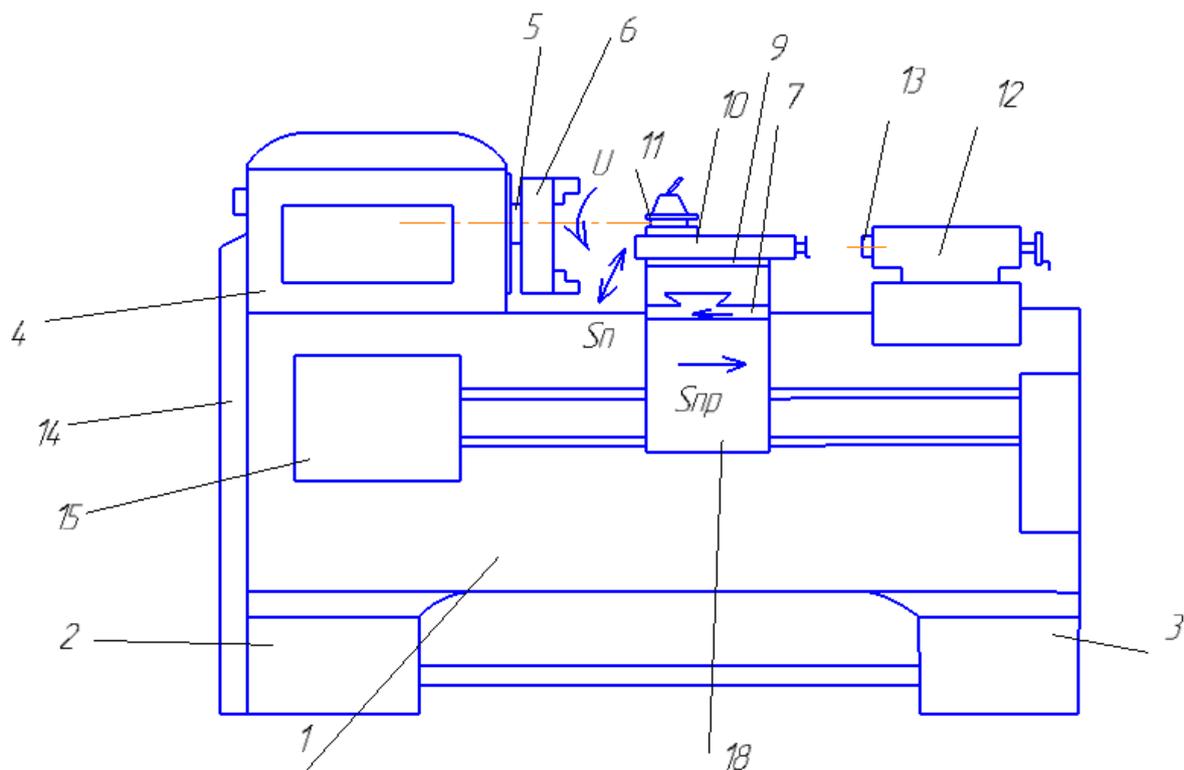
Компоновка токарно-винторезного станка 16К20
